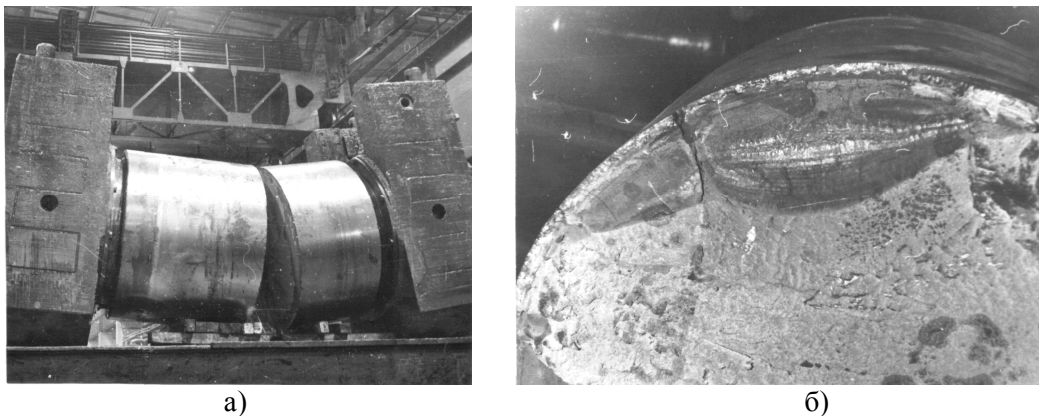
Усталостное разрушение наплавленного прокатного валка: а) – внешний вид валка с подшипниковыми узлами после разрушения; б) – макростроение зоны зарождения и распространения трещины
